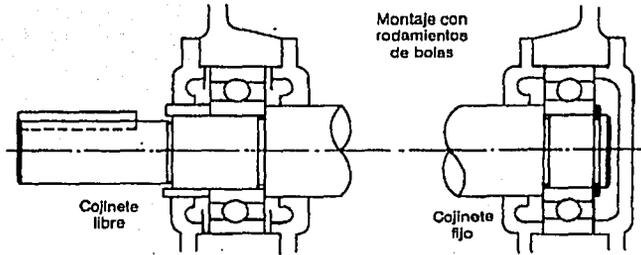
(montaje con cojinetes de rodamientos de una carrera de bolas o esferas, para motores pequeños; obsérvese la diferencia constructiva entre el cojinete libre y el fijo)
